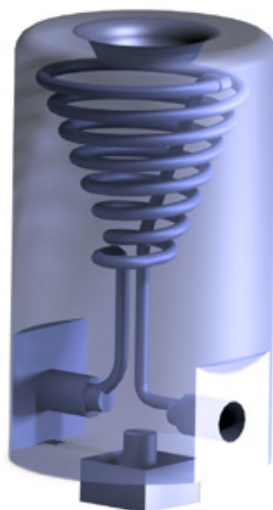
Einsatz für Spritzgießwerkzeuge. Bild: FH Wels
